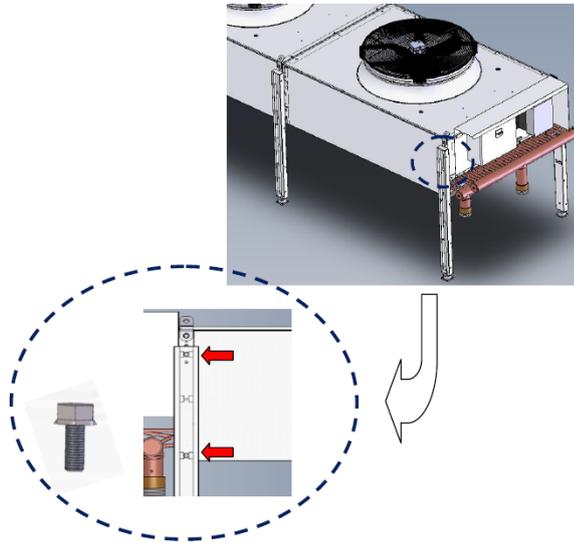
Schéma de montage des supports (rendu pour WTE800)
